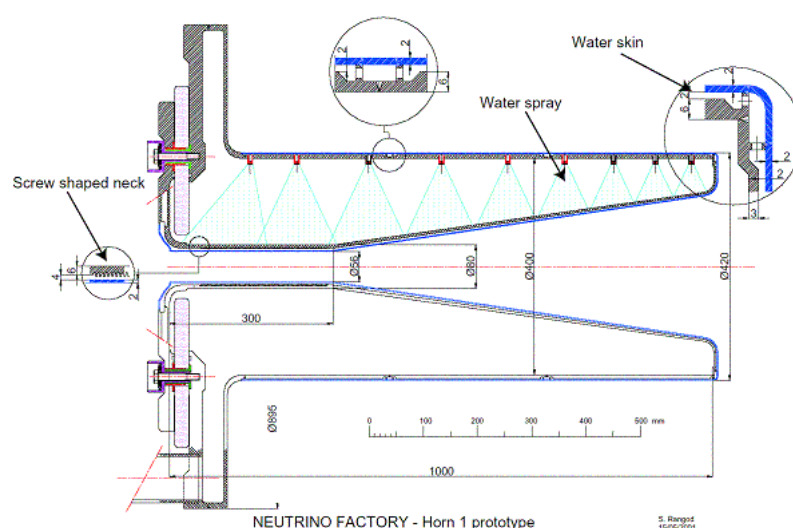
Plan du prototype de la corne construit au CERN.
